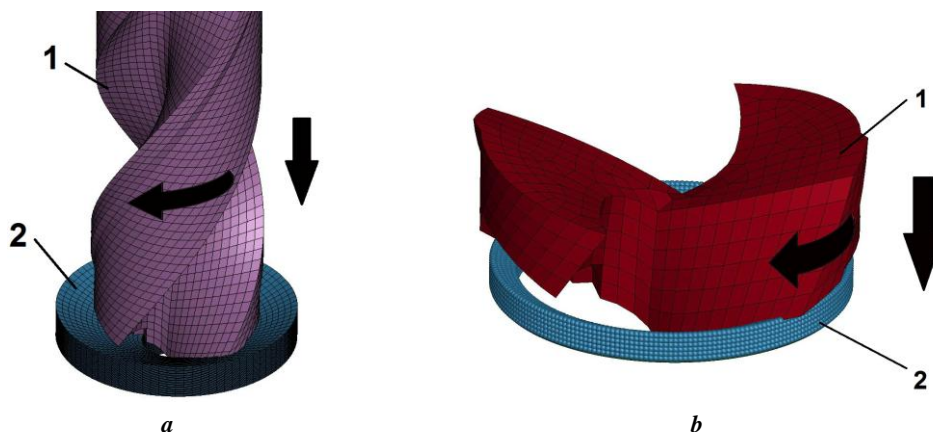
Схема процесса сверления цилиндрической заготовки методом Лагранжа (а) и трубной заготовки методом Галеркина (б): 1 – сверло, 2 – заготовка
